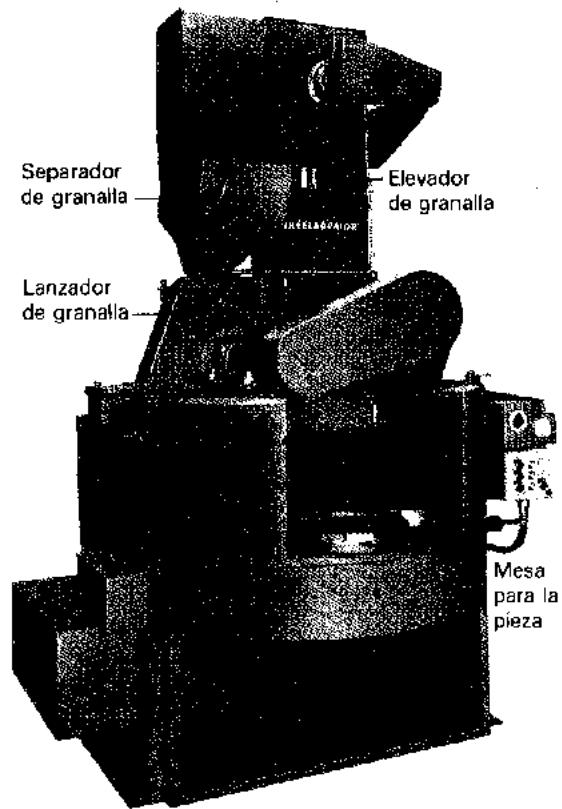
Máquina limpiadora por chorro, del tipo de mesa, y sus partes componentes (The Wheelabrator Corp.)
